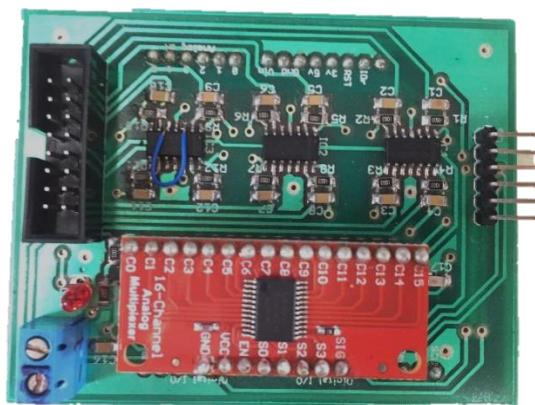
Tarjeta electrónica implementada con componentes soldados.
